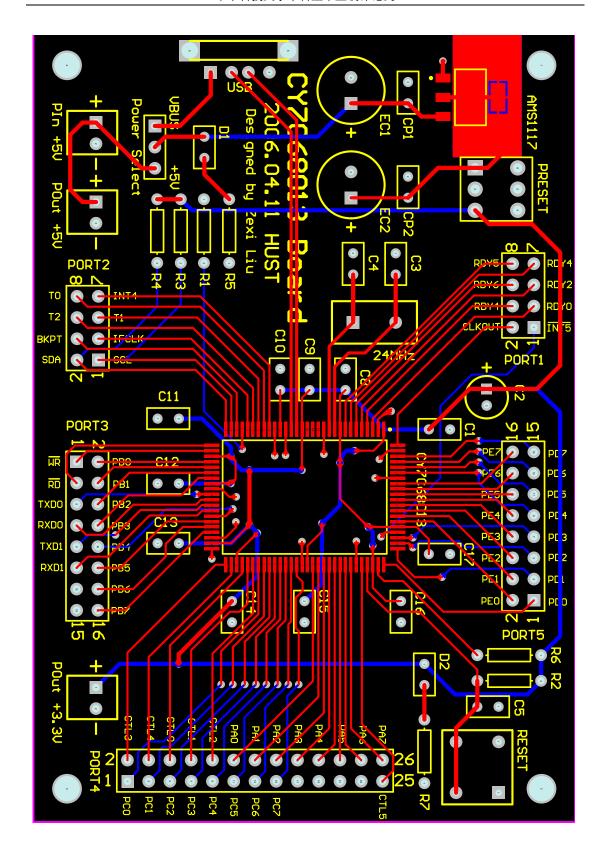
CY7C68013 扩展电路修改版 PCB 布线图
